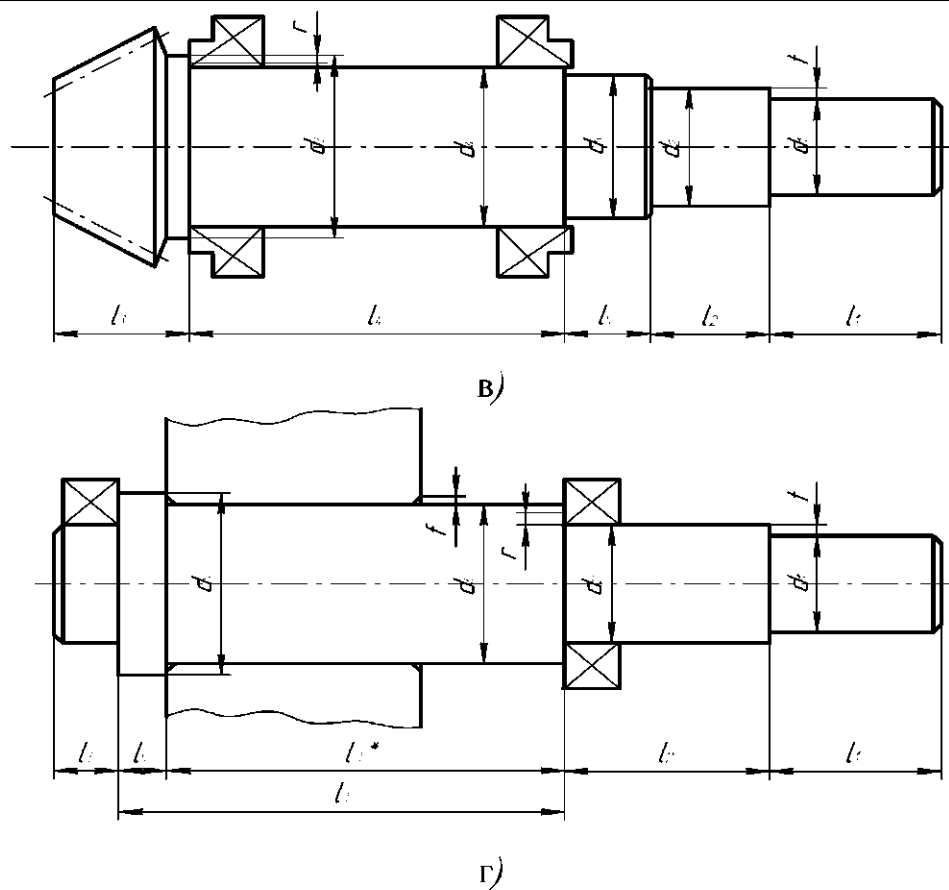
Типовые конструкции валов одноступенчатых редукторов:
